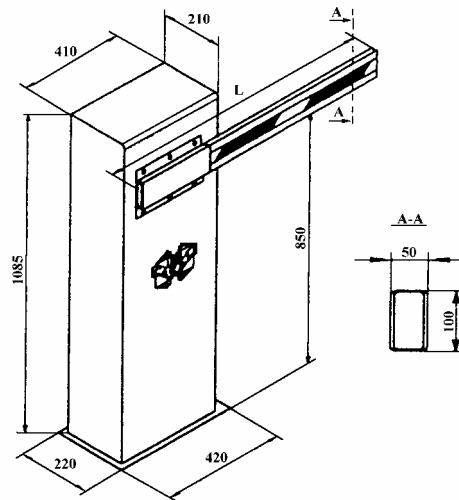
Габаритные размеры шлагбаума SPIN 6.
